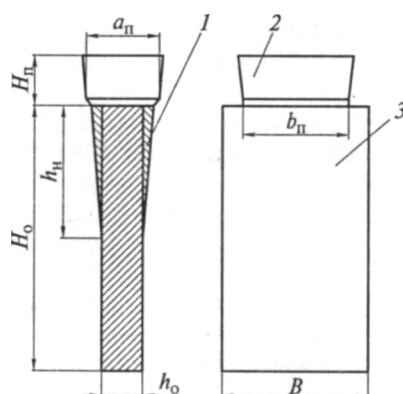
Технологический напуск на высоких отливках, заливаемых вертикально: 1 — технологический напуск; 2 — прибыль; 3 — отливка; a_n b_n — размеры прибыли в сечении; H_n — высота прибыли; B — ширина отливки; h_o — толщина отливки; H_o — высота отливки; h_n — высота напуска
